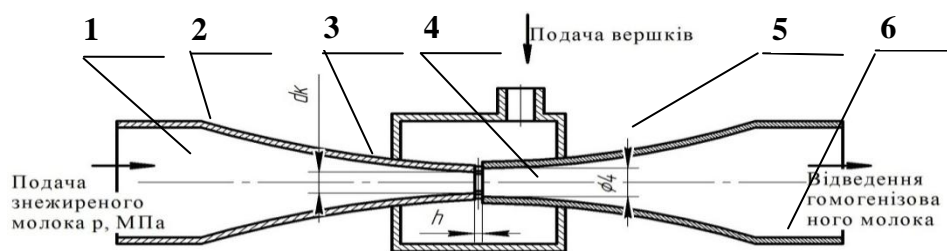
Схема робочої камери щілинного гомогенізатора молока струминного типу
